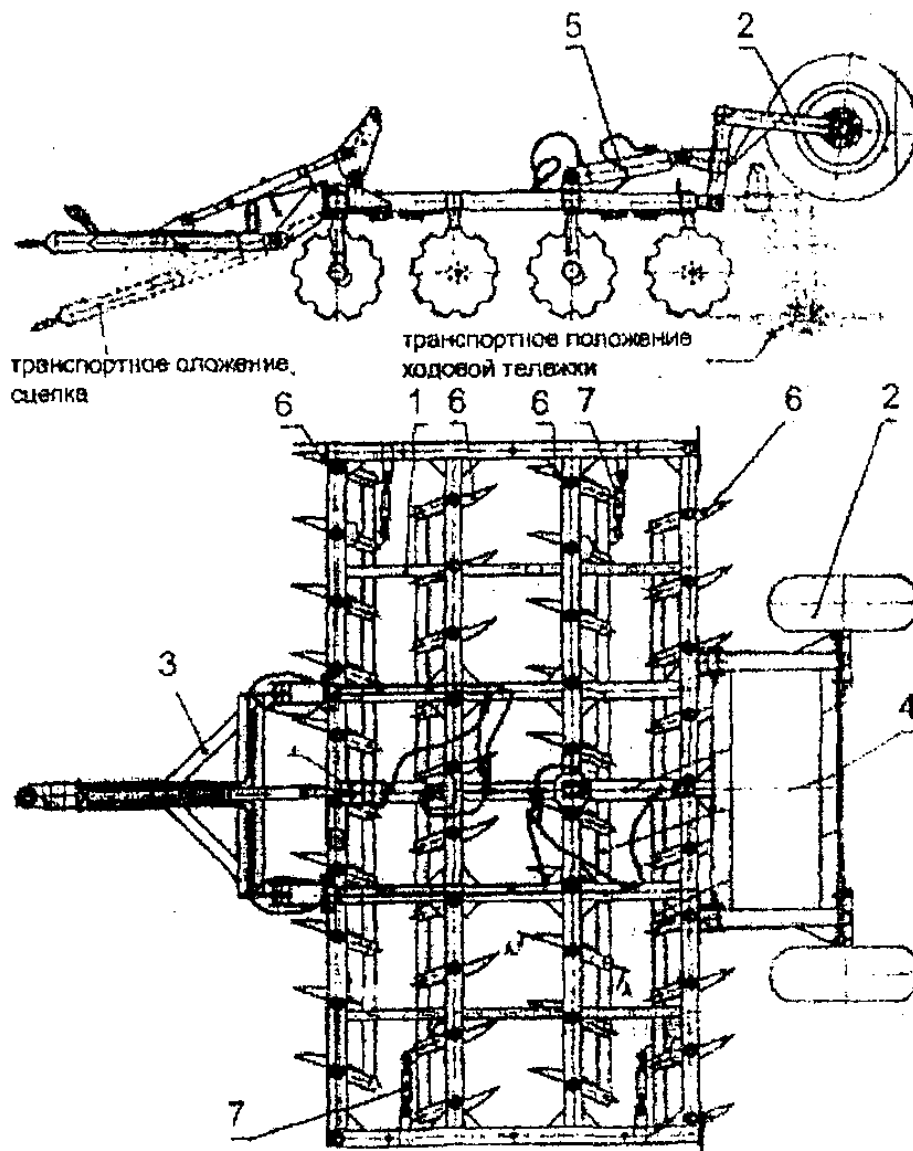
Схема бороны БДМ 4x4 (прицепной вариант): 1 – рама; 2 – колёса ходовые; 3 – сцепное устройство; 4 – тележка; 5 – гидросистема; 6 – режущий узел; 7 – механизм регулировки угла атаки дисков
